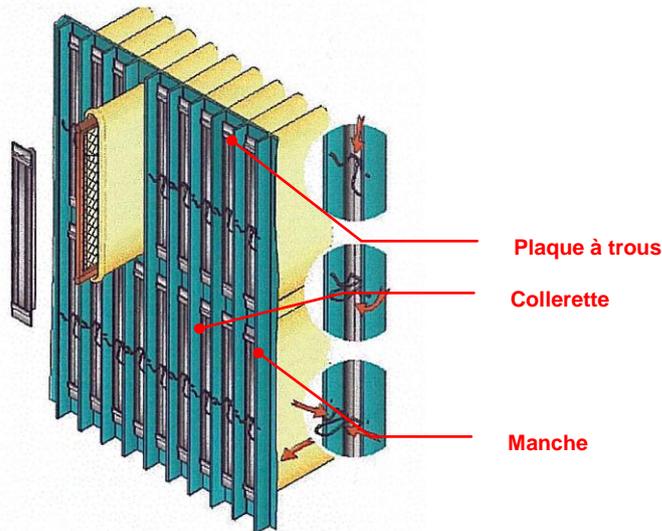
Manches plates horizontales et leur support (Source WEISS)
